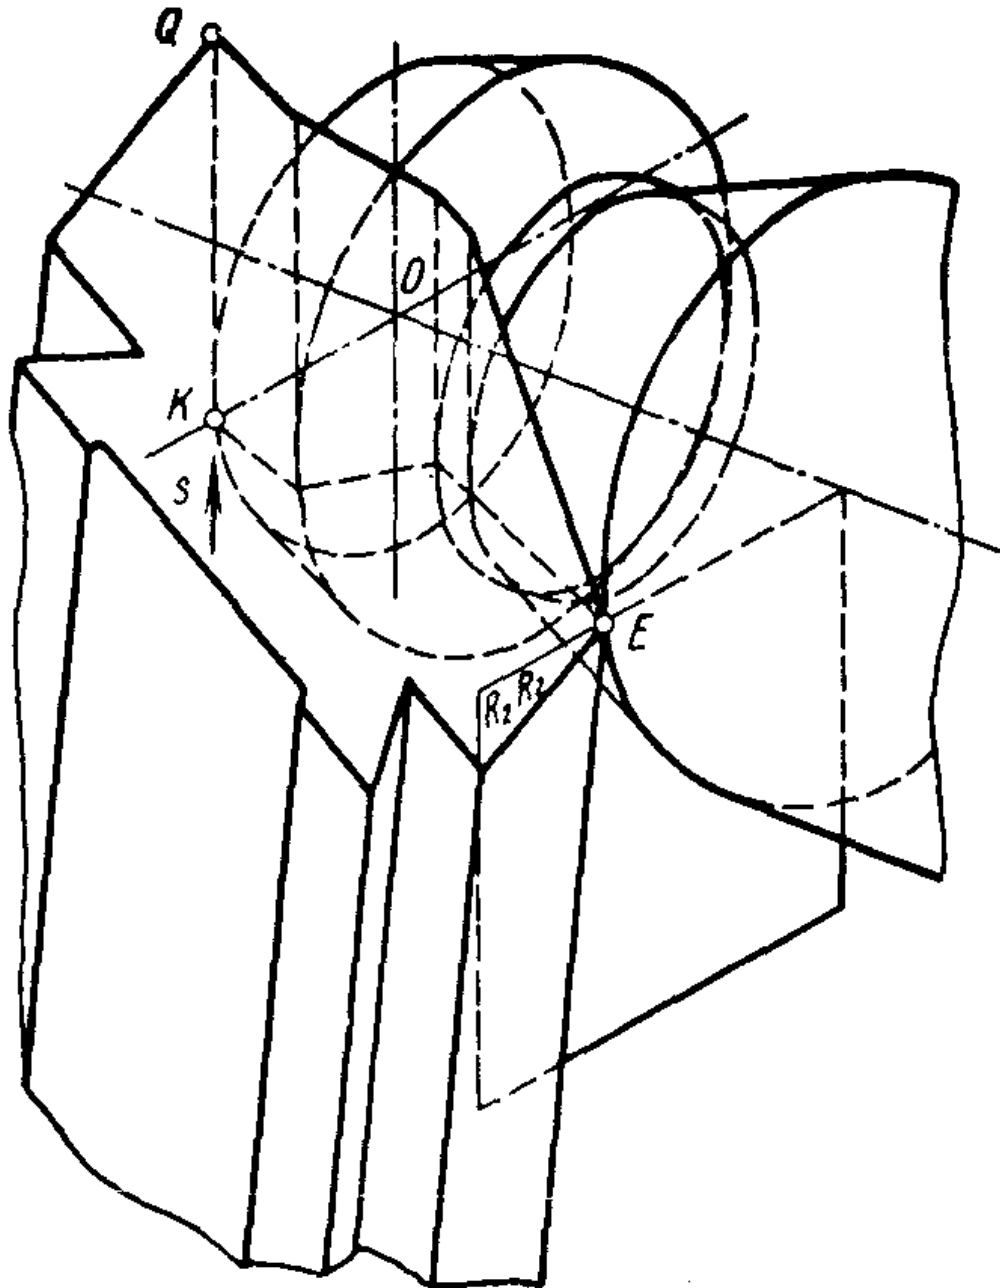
Схема різання тангенціальним різцем; всі різальні леза різця від точки Q до точки E вийшло з контакту з обробною деталлю; деталь оброблена
